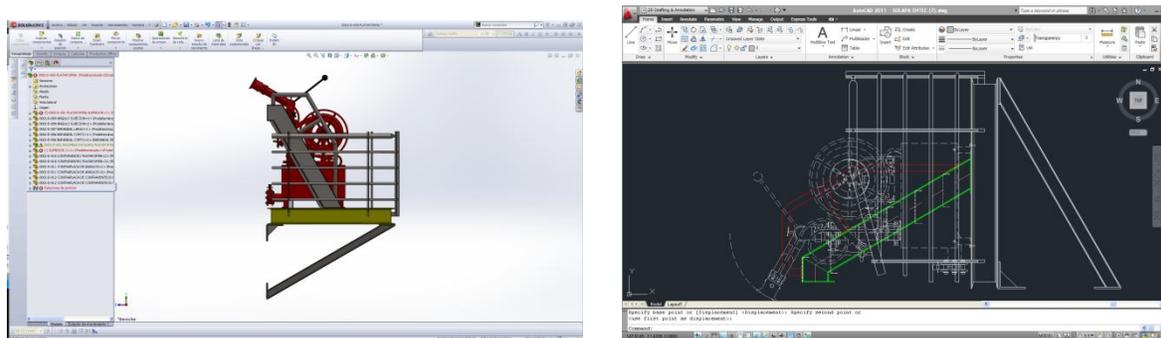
Vista lateral de la Plataforma del Supresor de Fuego. SolidWorks y Autocad
